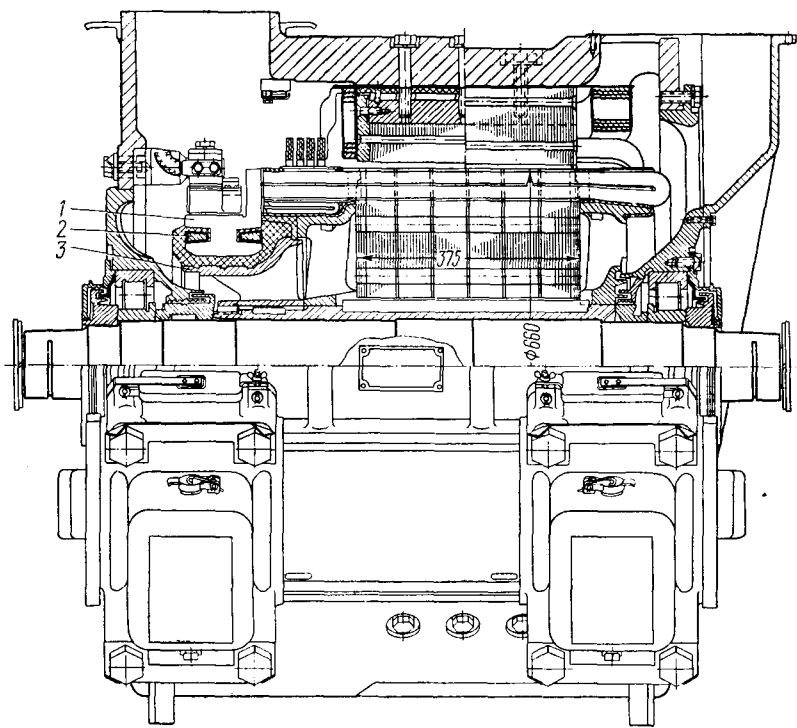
Продольный разрез тягового двигателя НБ-420Б
